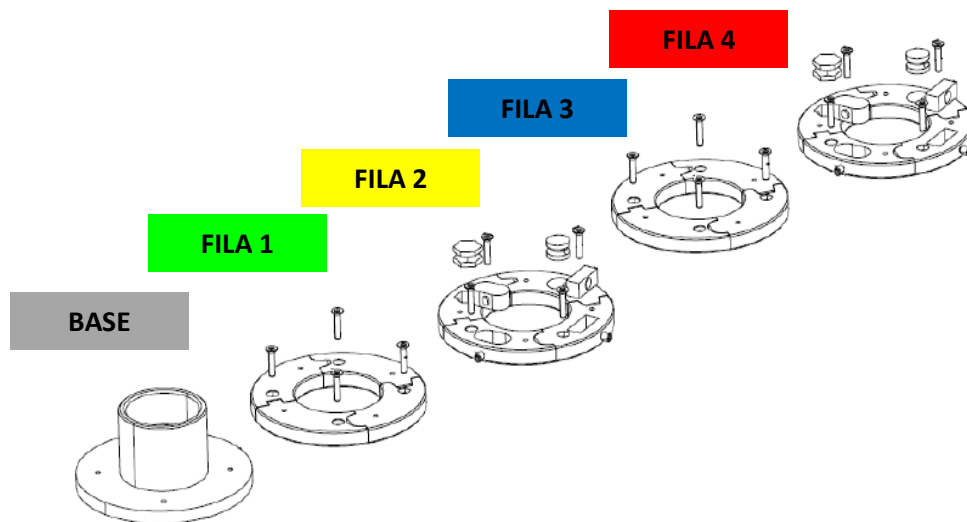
Solectron: Croquis del montaje (Renault-Nissan Consulting [3])
